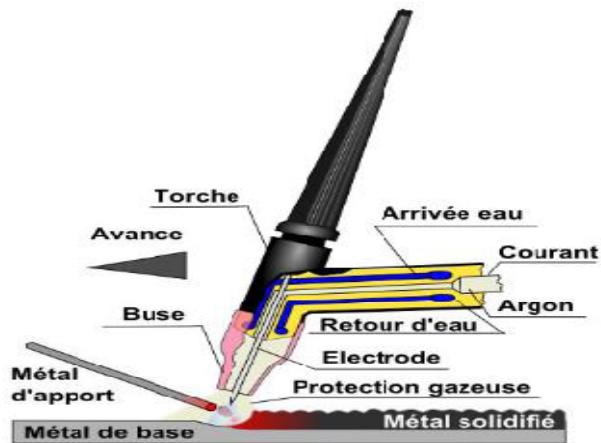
Principe du procédé de soudage TIG [23]
